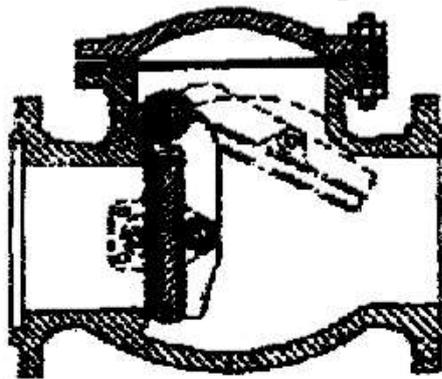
Поворотный обратный клапан D_y 50–600 мм
